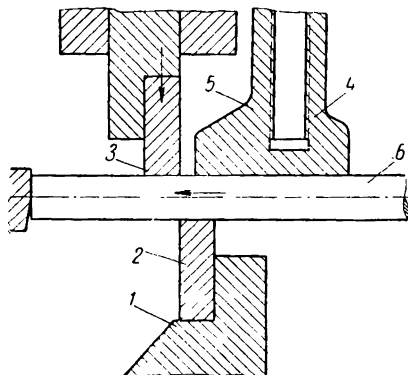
Схема резки с консольным прижимом: 1 — опора нижнего ножа; 2 — нижний нож; 3 — верхний нож; 4 — консольный прижим; 5 — прут
